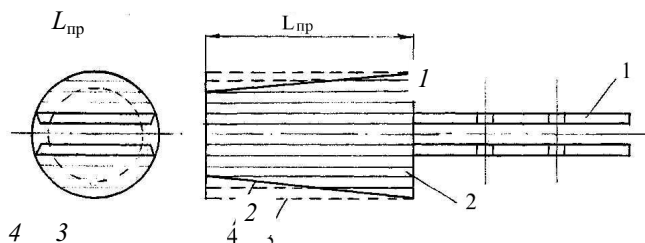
Пробка: 1 – выпуски из ДСП-Б; 2 – фанера, фанерные плиты или ДСП-Б (склеенные); 3 – форма заготовки; 4 – обточка на конус
